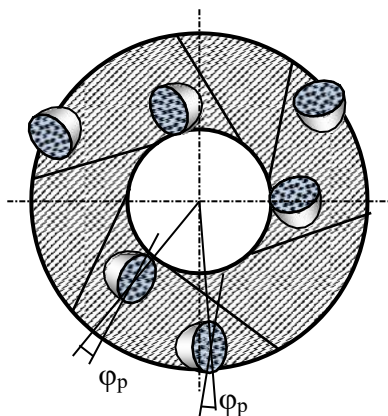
Схема установки резцов с *PDC* на торце инструмента для обеспечения отрицательного угла резания со скважинно- и кerno-образующими боковыми поверхностями
